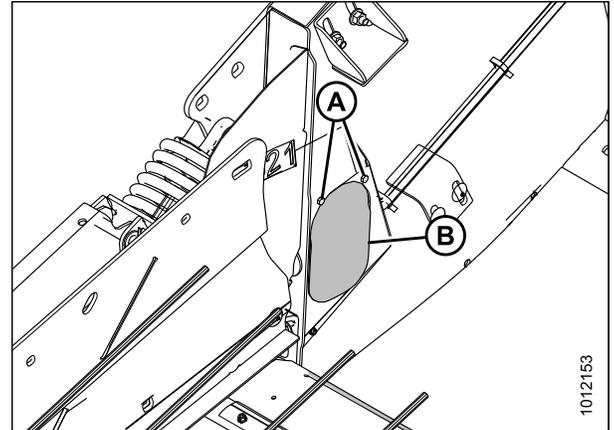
Ensamble del sensor de altura de la plataforma; lado izquierdo
